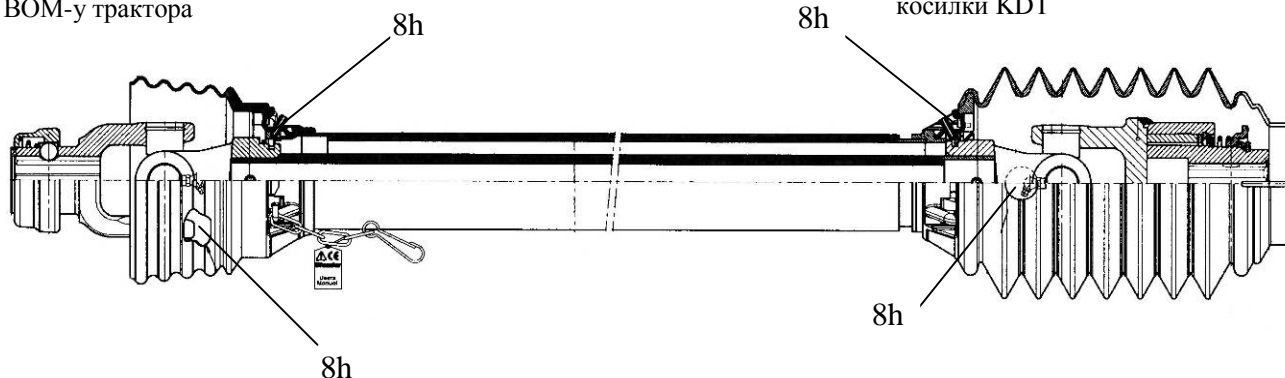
Подсоединение и смазка карданного вала «Weasler».
